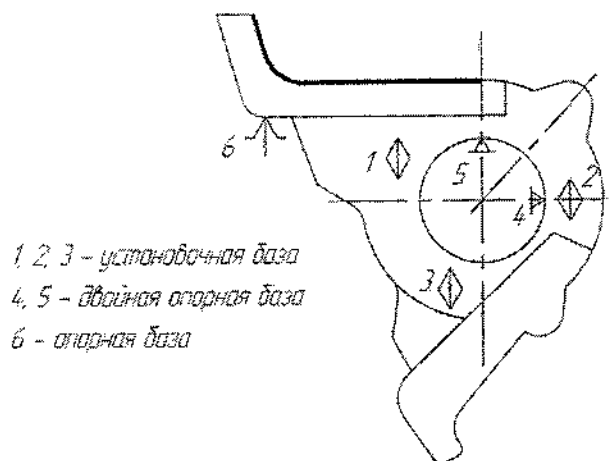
Схема базирования для фрезерной операции с ЧПУ
